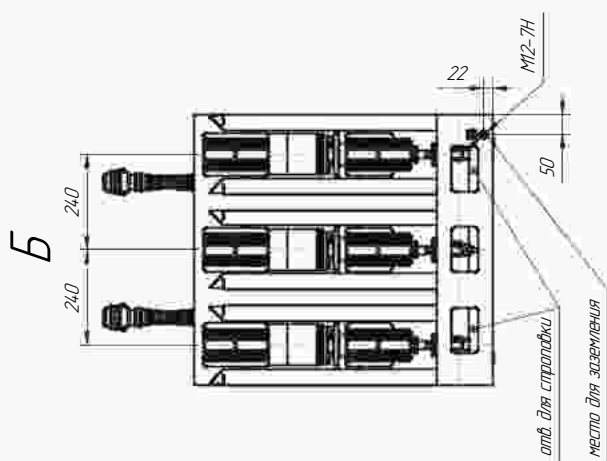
Габаритные, присоединительные и установочные размеры ВВУ-СЭЩ-П4-10-20/1000(1600)
